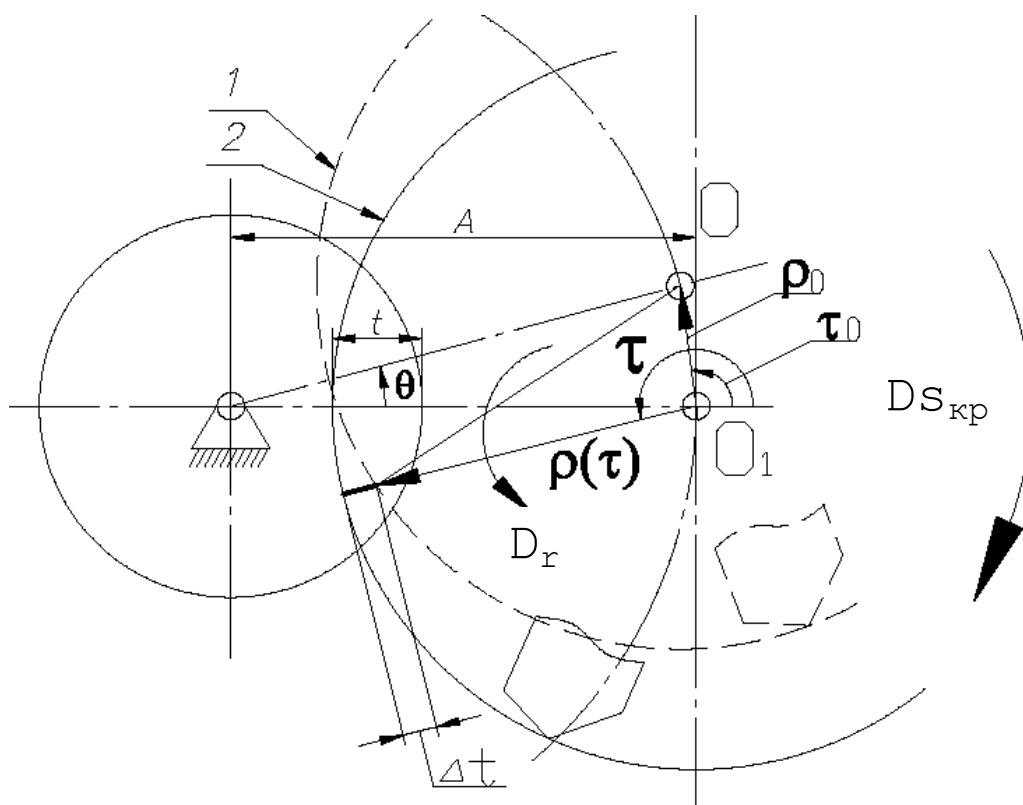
Схема прорезания трубной заготовки при получении винтовых рядов щелей:
